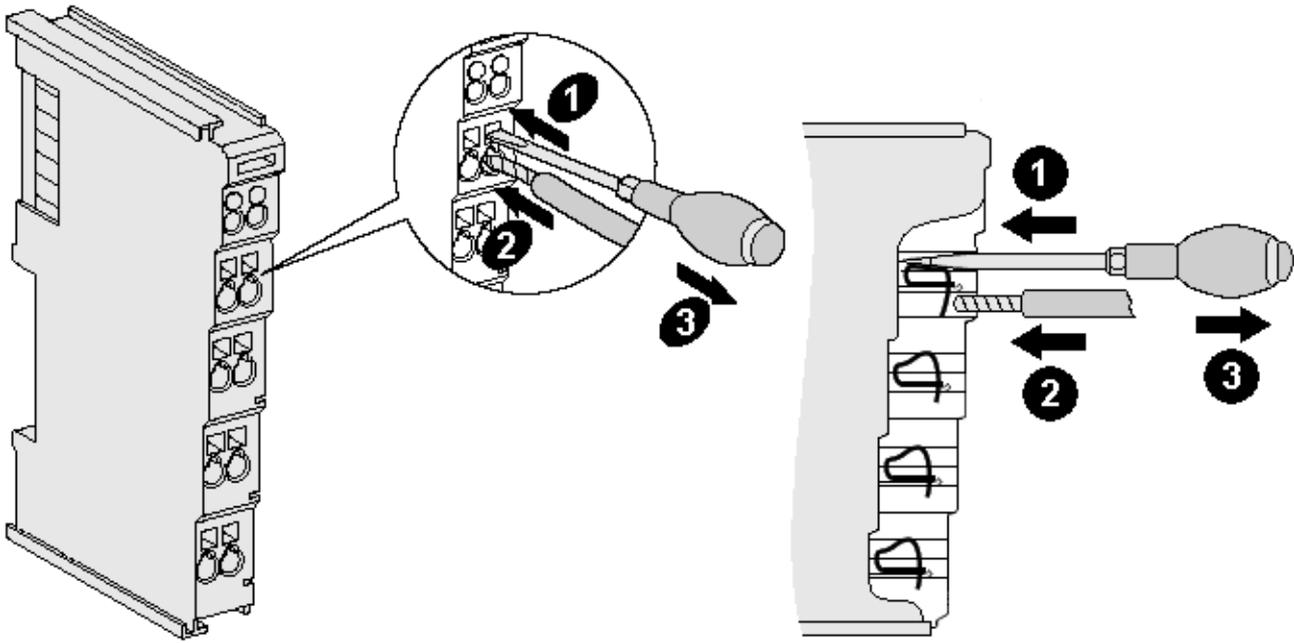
Anschluss einer Leitung an eine Klemmstelle
